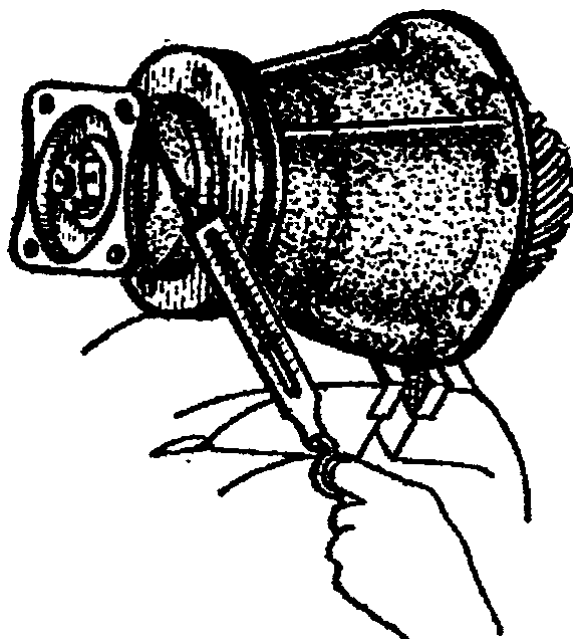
Перевірка затяжки підшипників вала ведучої конічної шестірні
